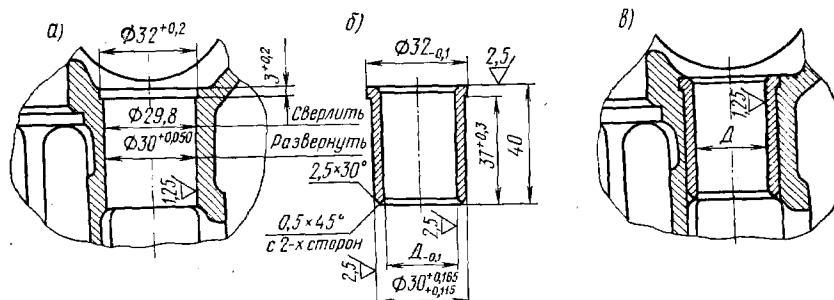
Размеры отверстий под толкатели при ремонте постановкой втулки
